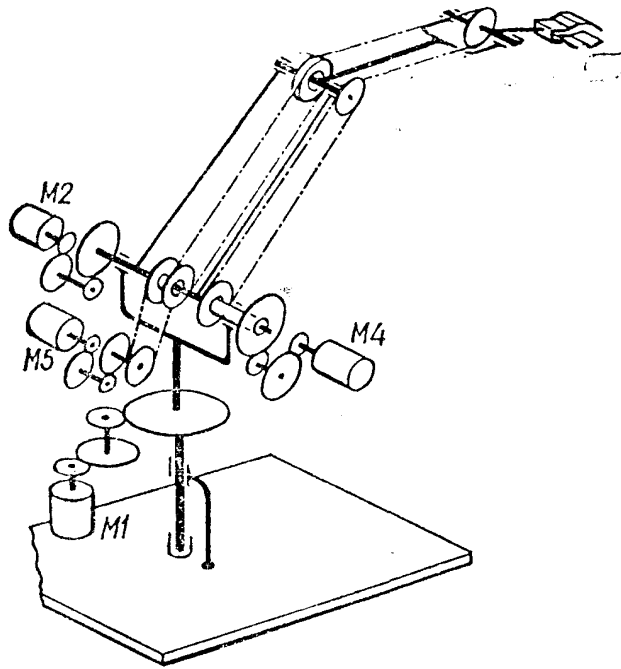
Die Hebelgestaltung des Manipulators mit der Kettengetriebe
